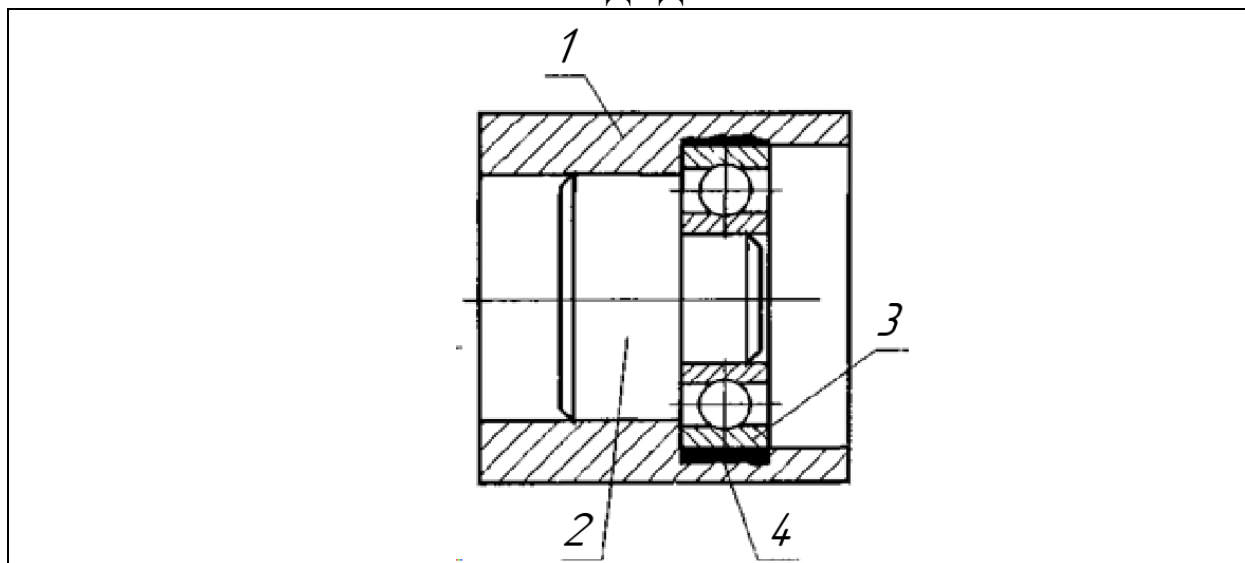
Відновлення поверхні нероз'ємного корпусу підшипника за використання центруючого пристрою: 1 – корпус, 2 – центруючий пристрій; 3 – підшипник; 4 – металополімерний матеріал
